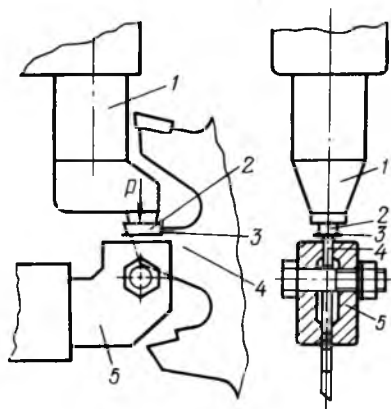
Схема пайки твердосплавной пластины при нагреве припоя в электродах машины для сваривания:
